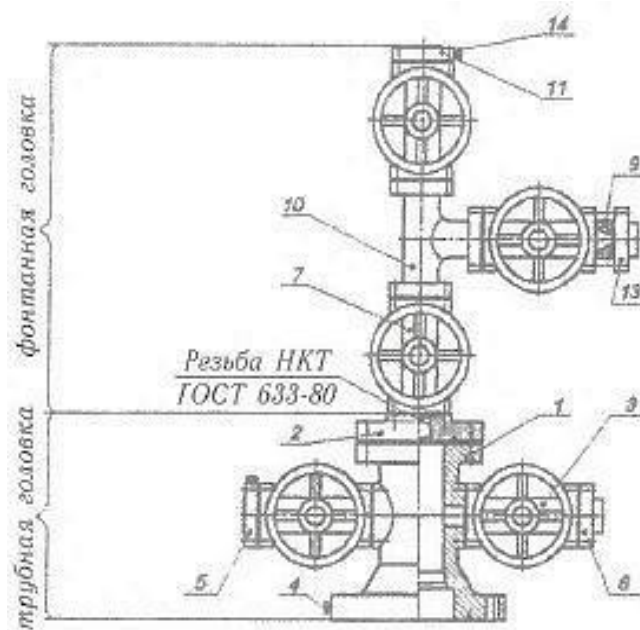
Схема арматуры нагнетательной АНК 65х21
